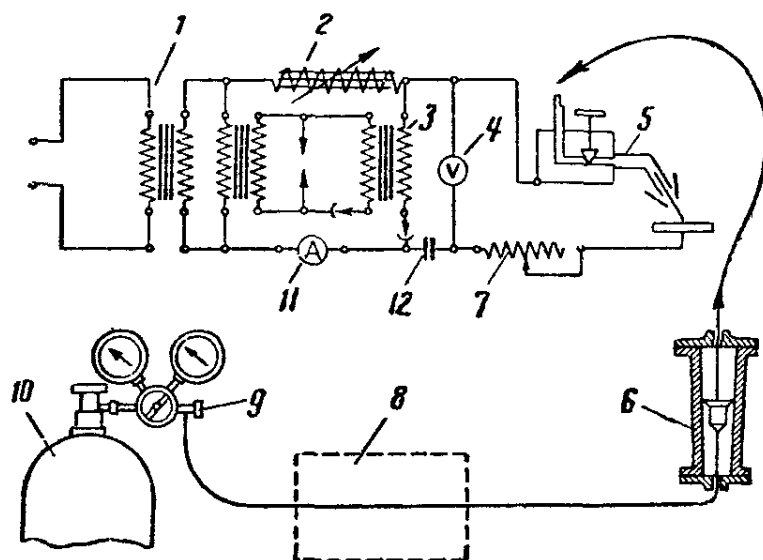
Схема установки для аргоно-дуговой сварки на переменном токе:
